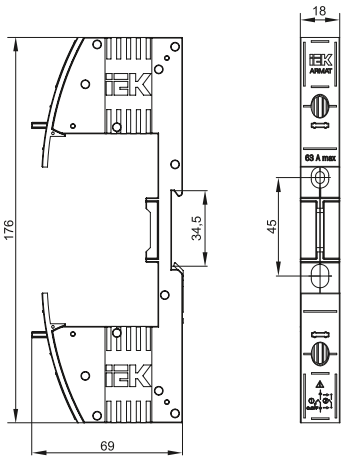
Габаритные и установочные размеры / Figure 1 – Overall and mounting dimensions
